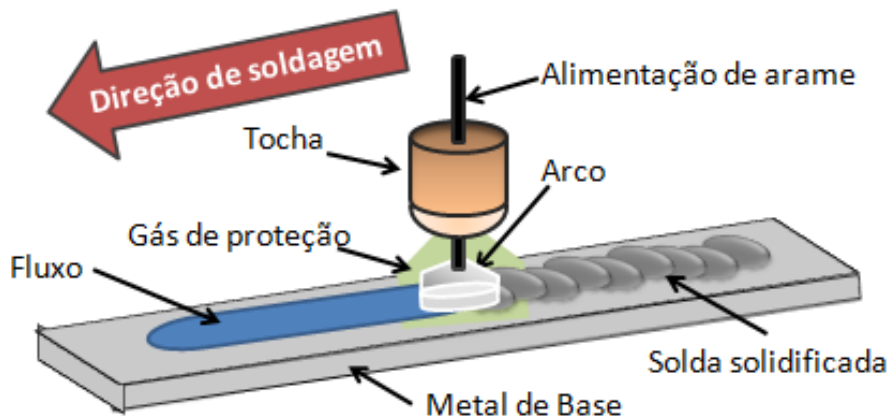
Esquema representativo da soldagem pelo processo MIG/MAG de um corpo de prova em que foi depositado uma camada de fluxo ativo.
